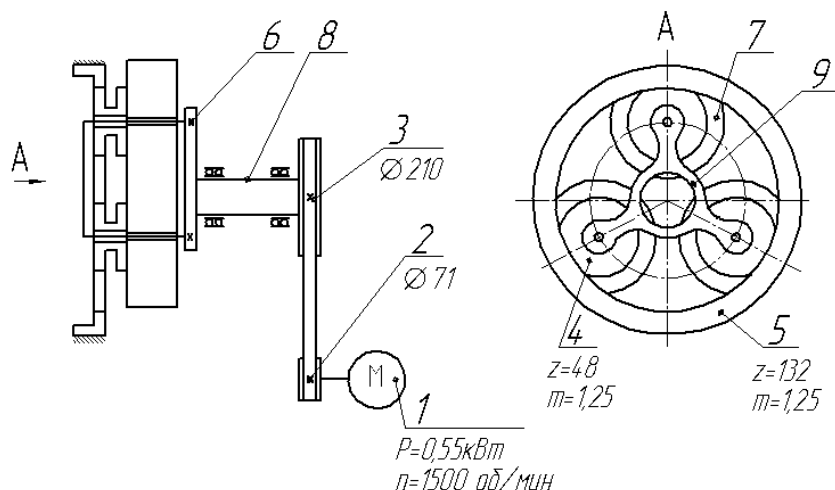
Кинематическая схема привода шлифовальной головки: 1 – электродвигатель, 2, 3 – шкивы, 4 – сателлит, 5 – коронная шестерня, 6, 9 – водило, 7 – шлифовальный лепестковый круг, 8 – полый вал
